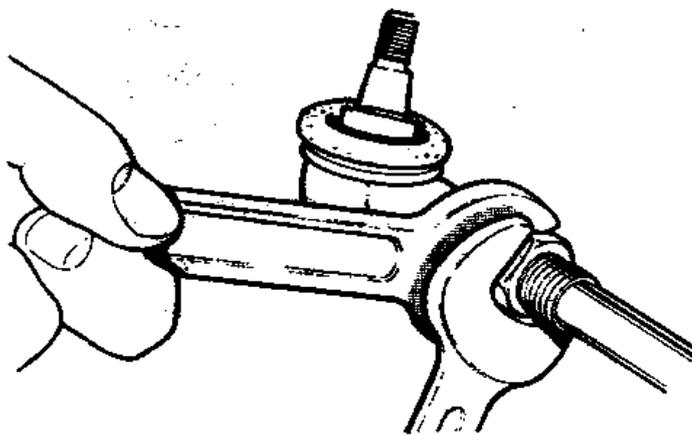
Ослабление контргайки наконечника рулевой тяги (Разд.35)
